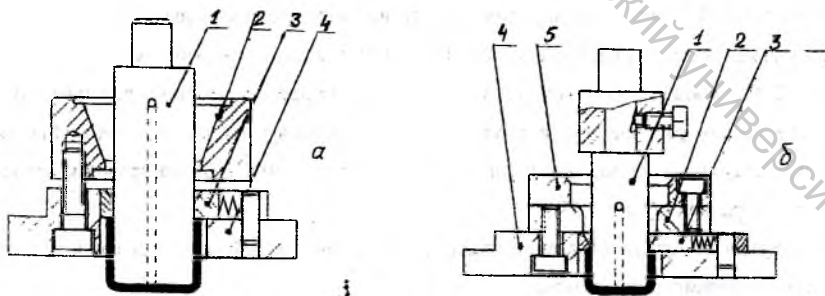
Пакеты штампов для вытяжки без прижима (на провал)
